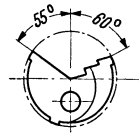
Tieflochbohrer mit eingebohrtem Ölloch und angeschweißtem Rohrschaft. 20...60 mm \varnothing .
